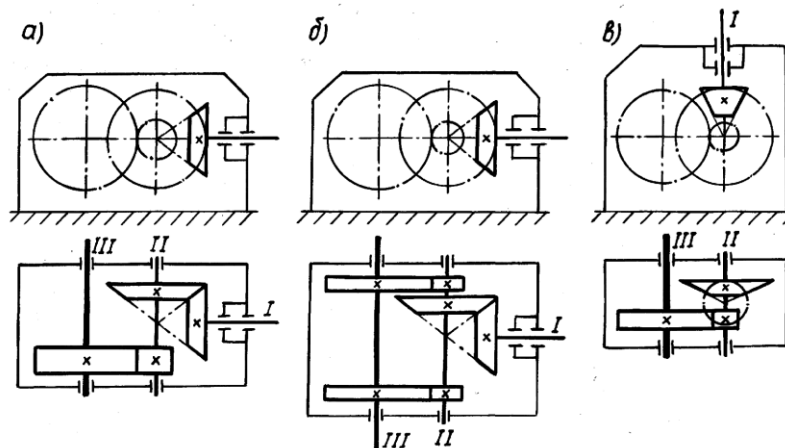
Кинематические схемы двухступенчатых коническо-цилиндрических редукторов: I, II, III – соответственно быстроходный, промежуточный и тихоходный валы
